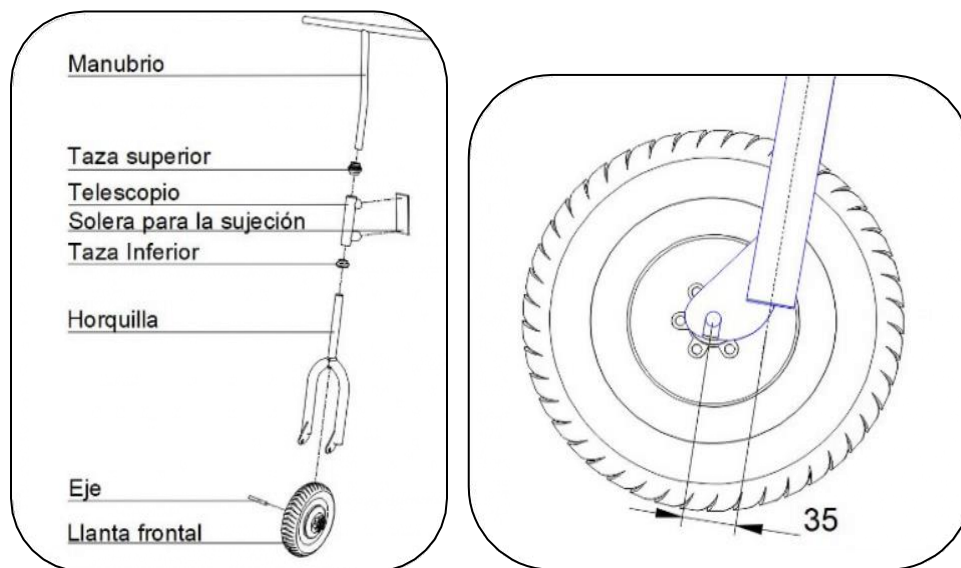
Explosivo del sistema de dirección (Izquierda), offset de la horquilla de 35mm (derecha).
